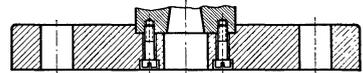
Befeestigung der Schnittplatte durch Zugschrauben und Einsenkung.
